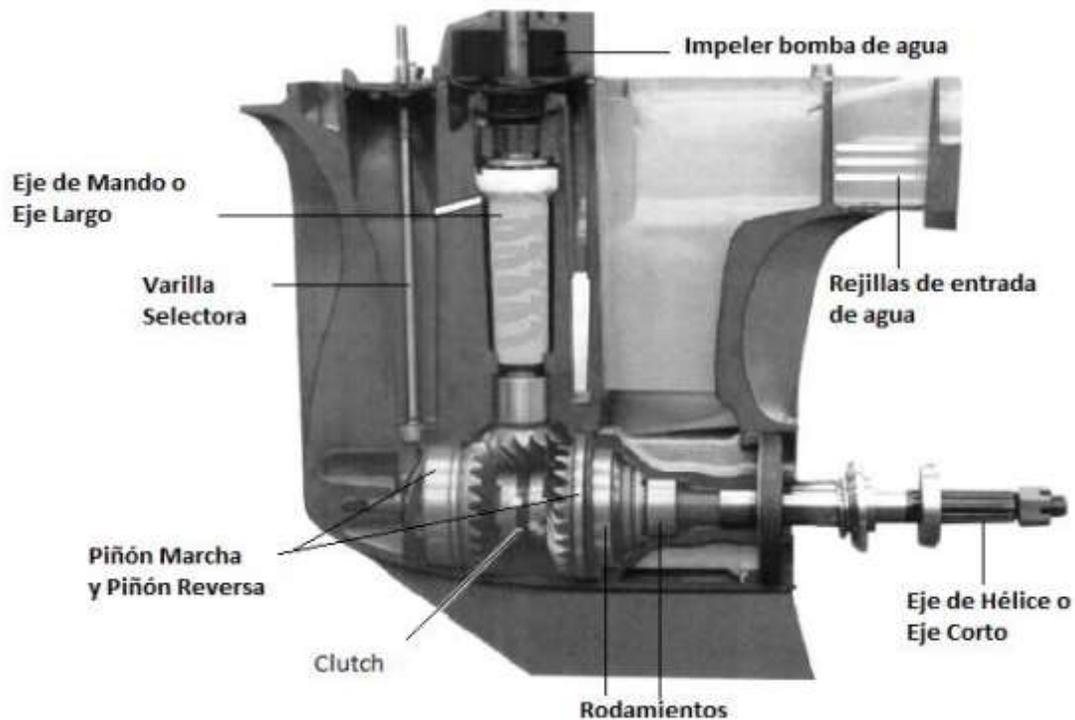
Interior de una transmisión en motor fuera de borda, con partes básicas.
